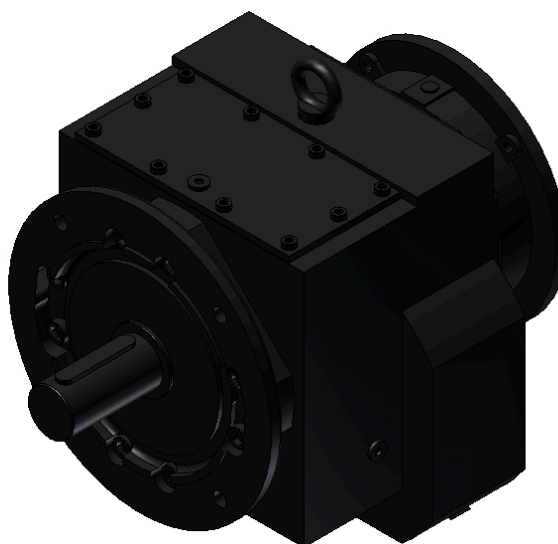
Elektromotor SIEMENS 1LA9113-4KA61-Z A11 [1]
